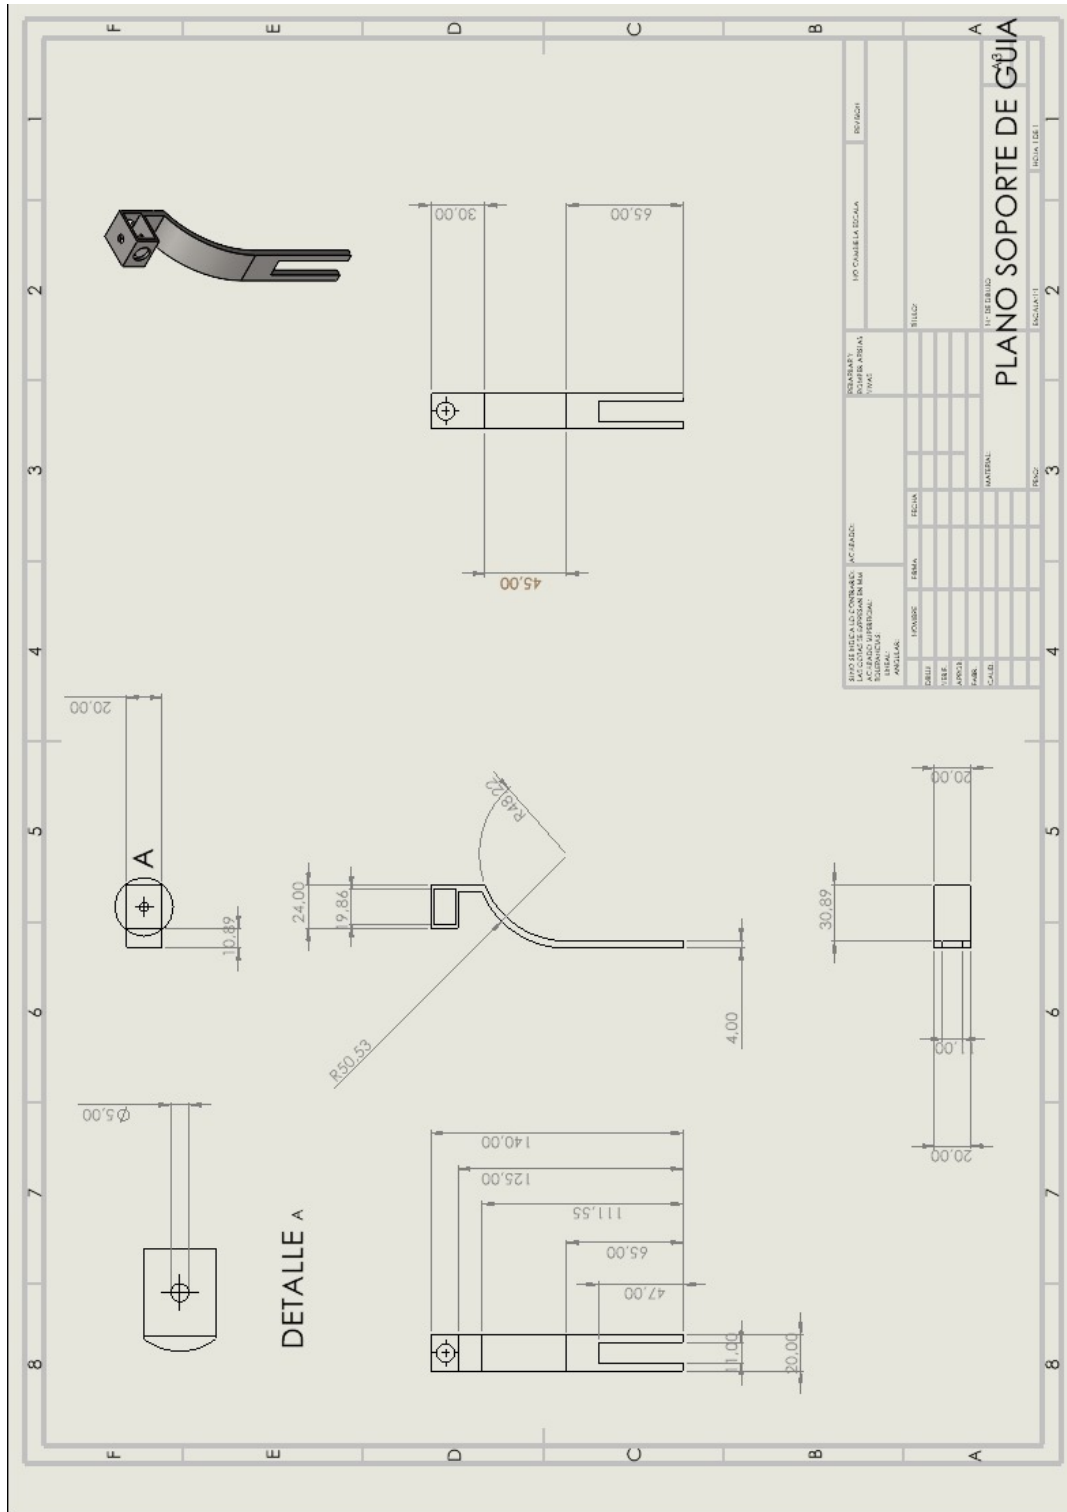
Plano soporte de guía. Fuente: Elaborado por autores.
